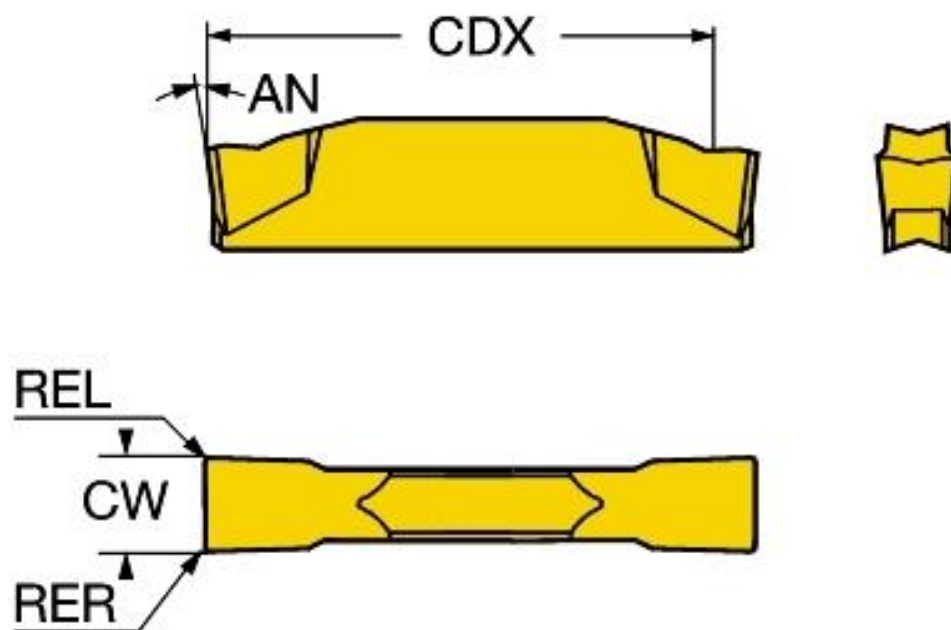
Пластина N123G2-0300-0003-CR
